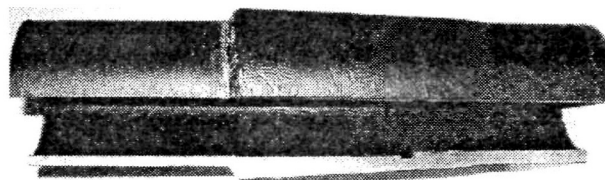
Сварное нахлестное соединение труб типа "НЗ"
